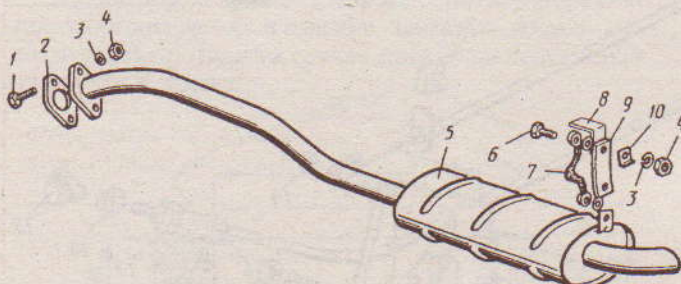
Глушитель выхлопа газов: 1 - болт М8; 2 - прокладка; 3 - шайба 8Т; 4 - гайка М8; 5 - глушитель выхлопа газов; 6 - болт М8; 7 - провод на "массу"; 8 - шайба 8; 9 - ремень подвески глушителя; 10 - усилитель хомута крепления бензинового бака
